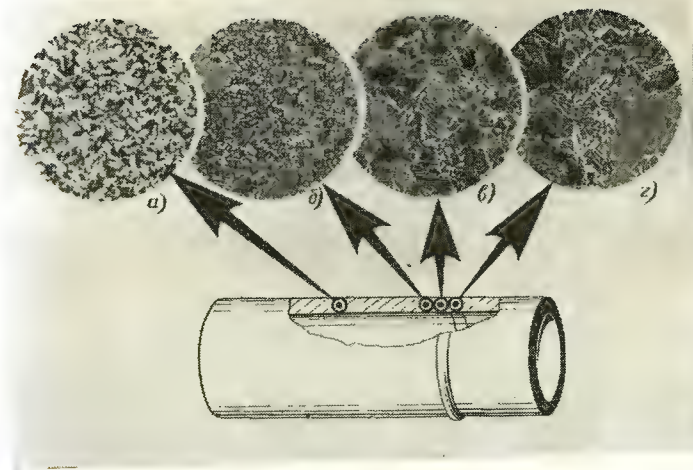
Структура металла у контактного сварного шва трубы диаметром $38 \times 4,5$ мм, изготовленной из стали марки 20 (увеличено в 50 раз.)
